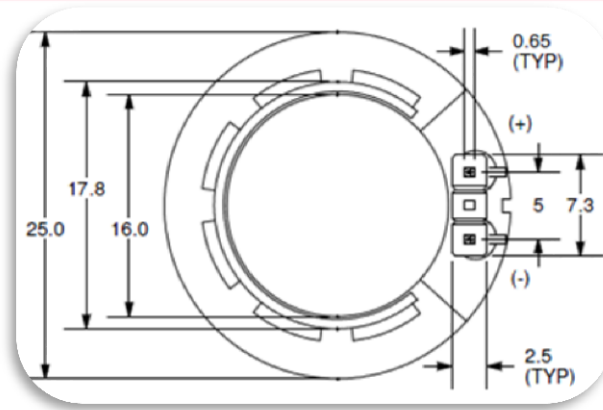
11: Dimensiones del parlante CLF0251MP (mm). Fuente: CUI Inc.
